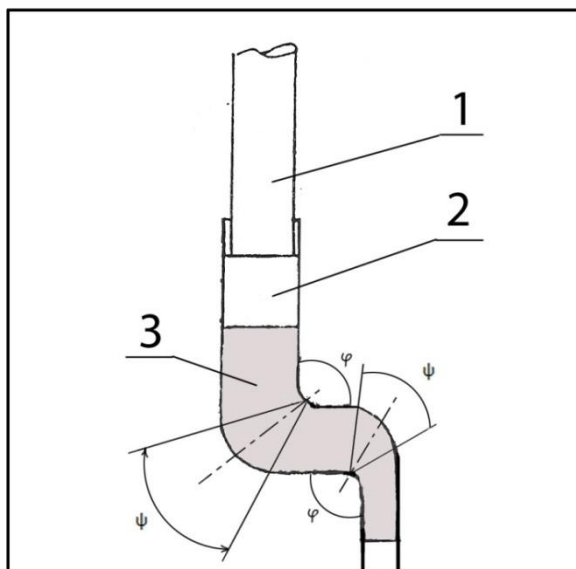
Схема оснастки РКУП (1 – пуансон; 2 – пресс-шайба; 3 – деформированный образец в процессе РКУП; φ , ψ – внутренний и внешний угол, соответственно).
